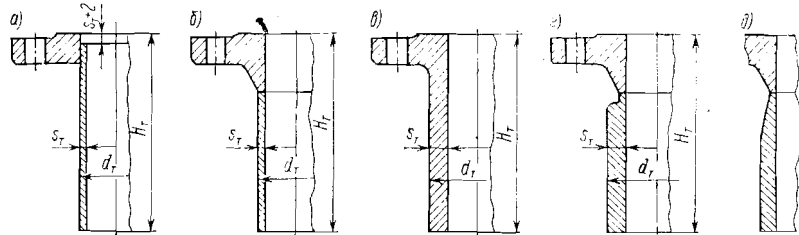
Конструкции стандартных стальных приварных фланцевых штуцеров: а — с приварным плоским фланцем и тонкостенным патрубком; б — с приварным фланцем встык и тонкостенным патрубком; в — кованый толстостенный; г — с приварным фланцем встык и толстостенным патрубком; д — вариант конструкции сварного толстостенного штуцера
